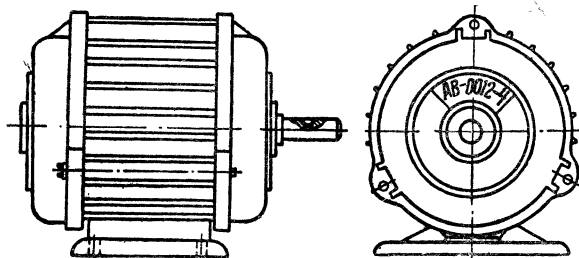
Закрытый двигатель типа АВ-0012-4.
